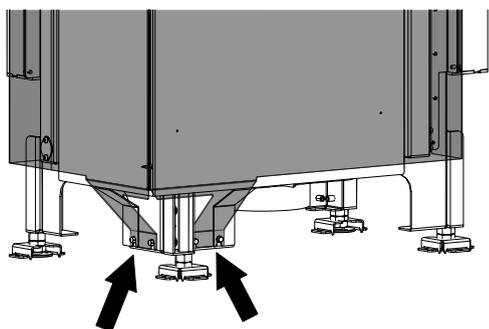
Poser l'arrière et le côté du kit de convection sur le foyer
